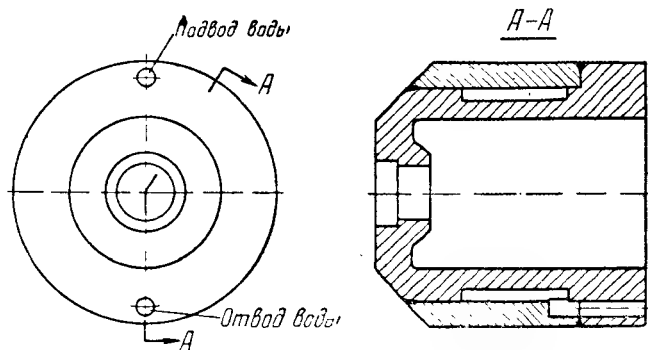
Кольцевой канал (рубашка) в корпусе для водяного охлаждения двигателя.
